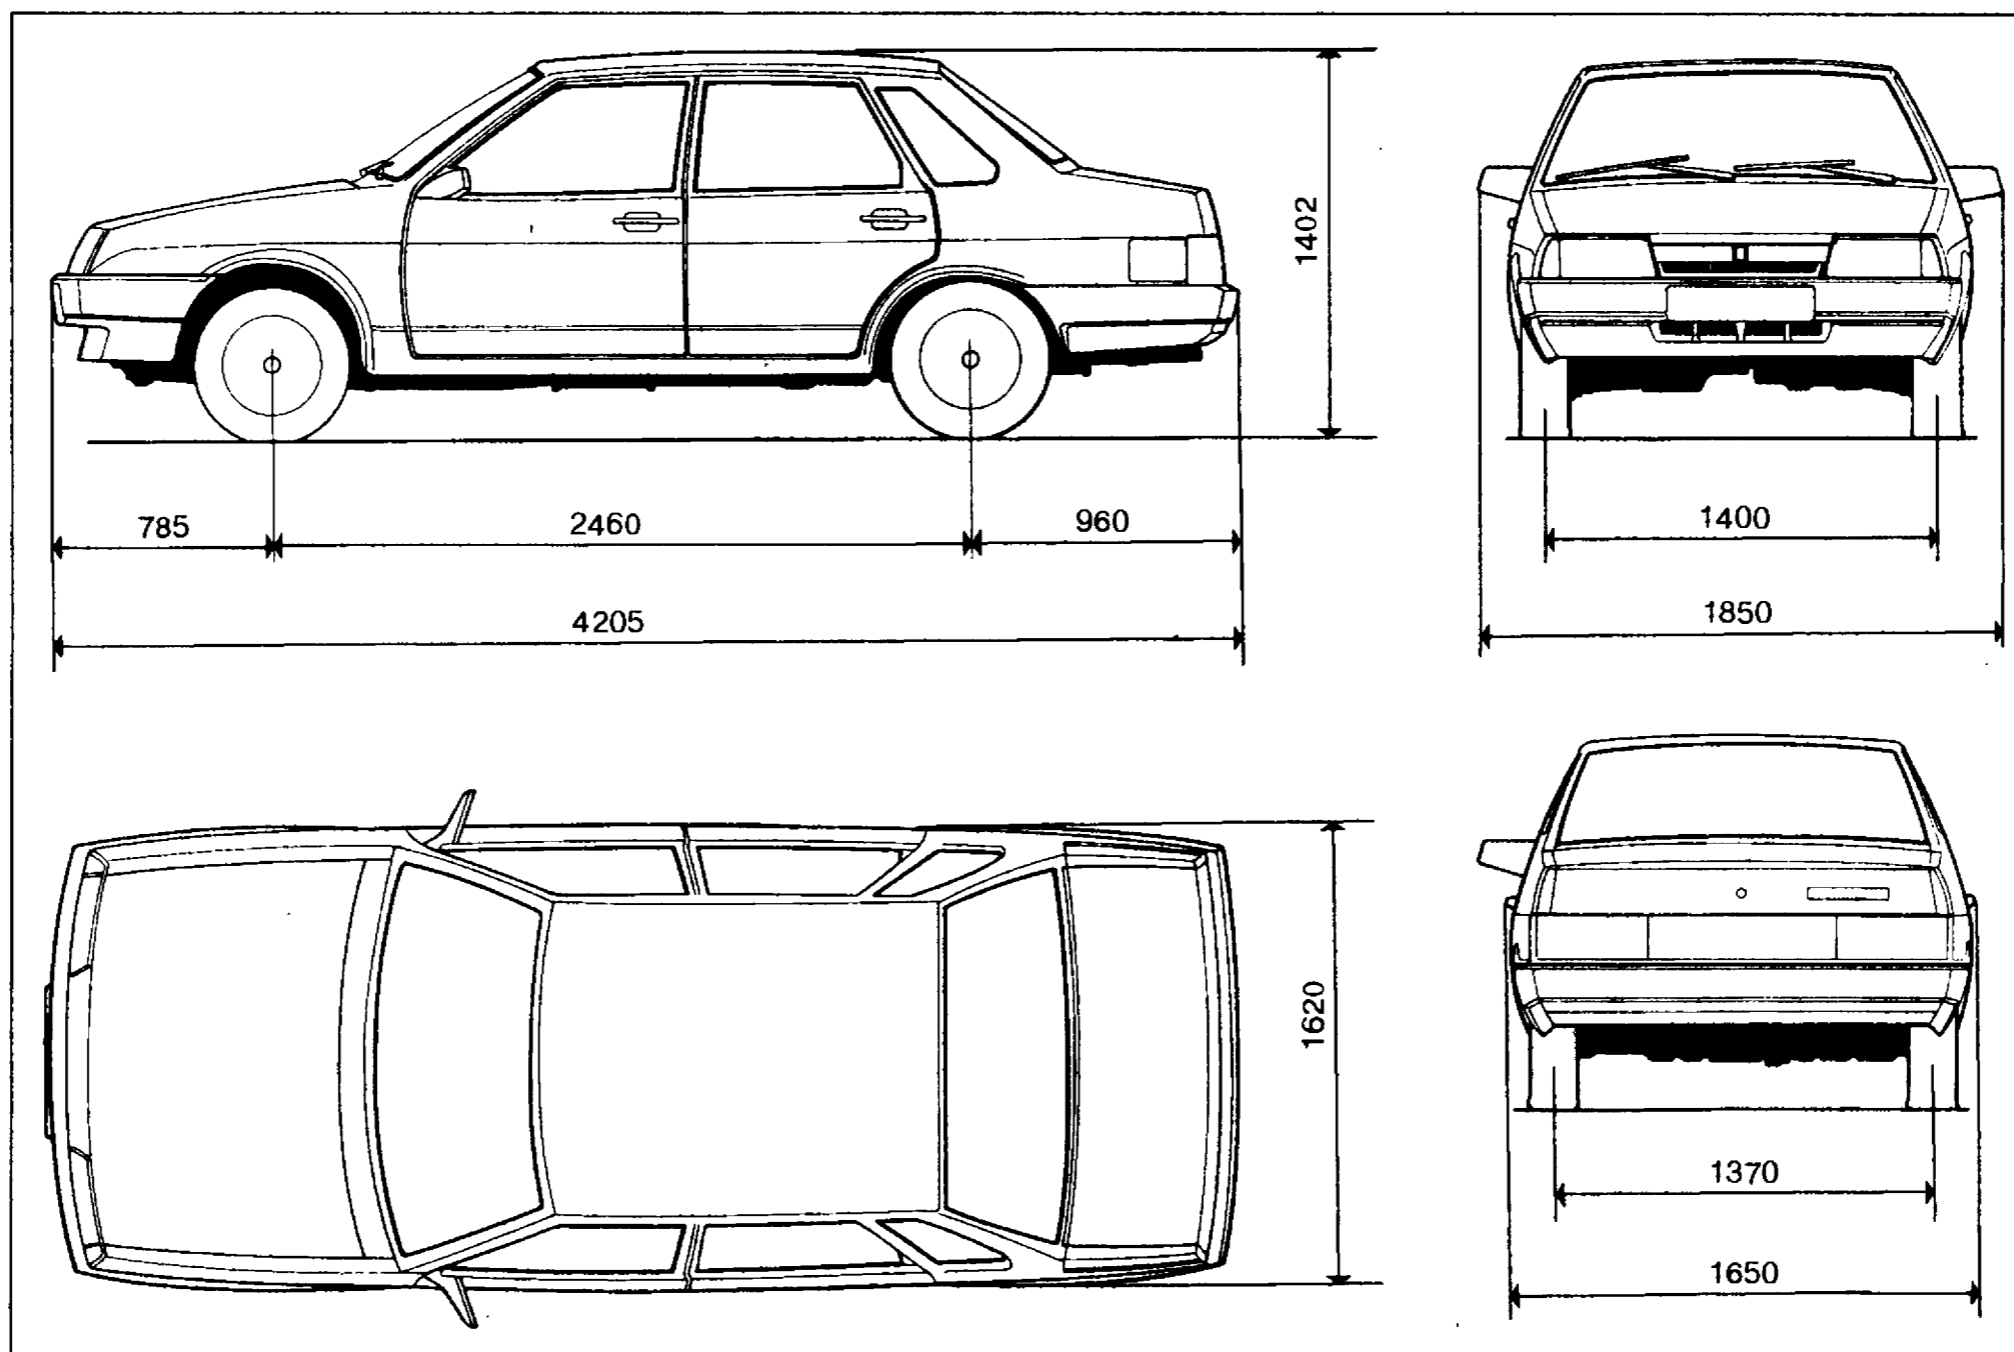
Габаритные размеры автомобиля ВАЗ-21099
